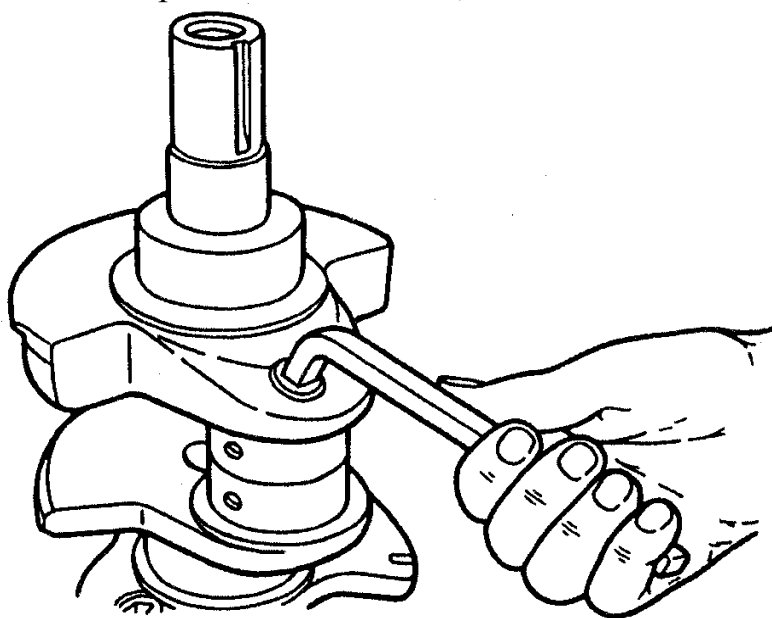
Вывертывание пробок грязеуловителей из коленчатого вала
